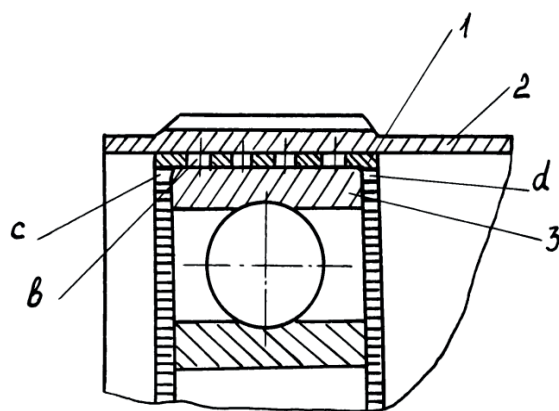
Конструкция с промежуточным кольцом для сочленения гибкого колеса с гибким подшипником (позиции в тексте)
